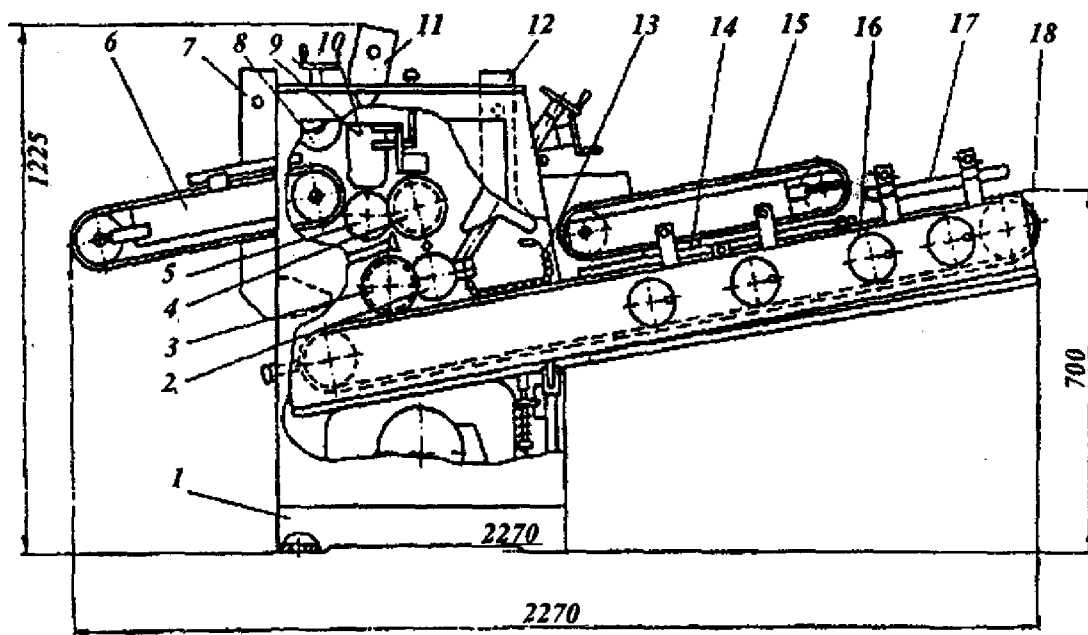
Тістозакатувальна машина Т1-ХТЗ-2-3:1 і 13 – транспортери: 2 – формувальна дошка; 3 - несучий транспортер; 4 - формувальний транспортер; 5 – напрямні; 6 – решітка; 7, 11, 12 -насадки для обдування робочих органів повітрям; 8 - валок; 9 -центрувальний пристрій; 10 - механізм регулювання; 14, 15, - розкатувальні валки, 16 – транспортер; 17 - формувальна дошка; 18 - станина з приводом.
